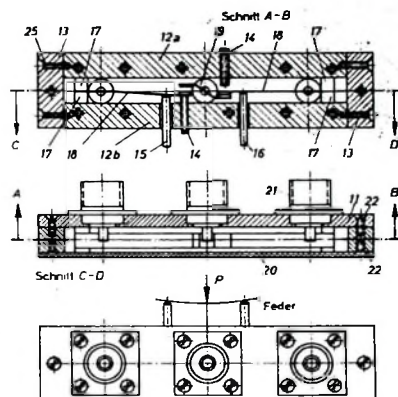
Schnittzeichnung des Koaxialumschalters Ausführung B
